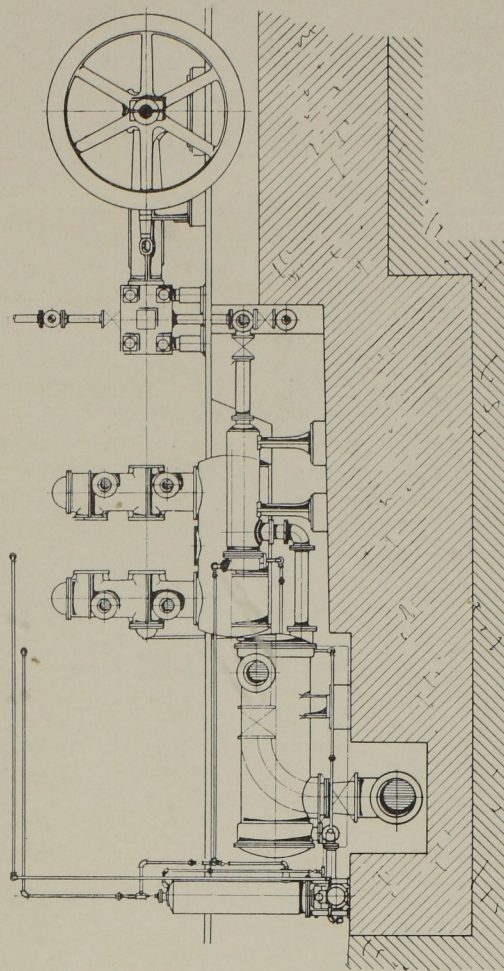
Seitenansicht der Pumpmaschine. Masst. 1 : 96.
